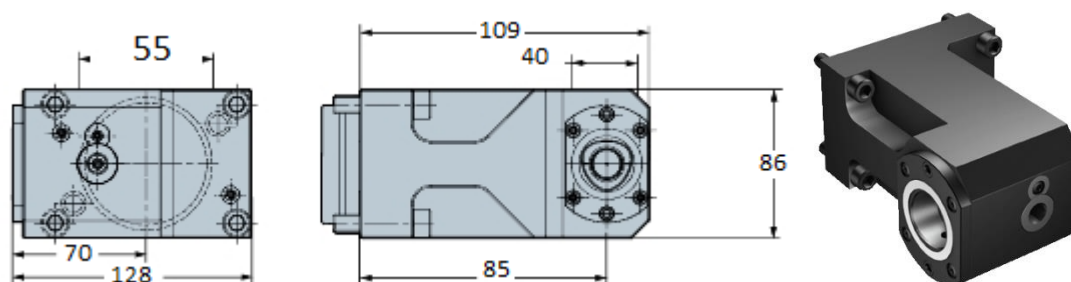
Инструментальный блок для ручного закрепления С4-TRI-OK55А
